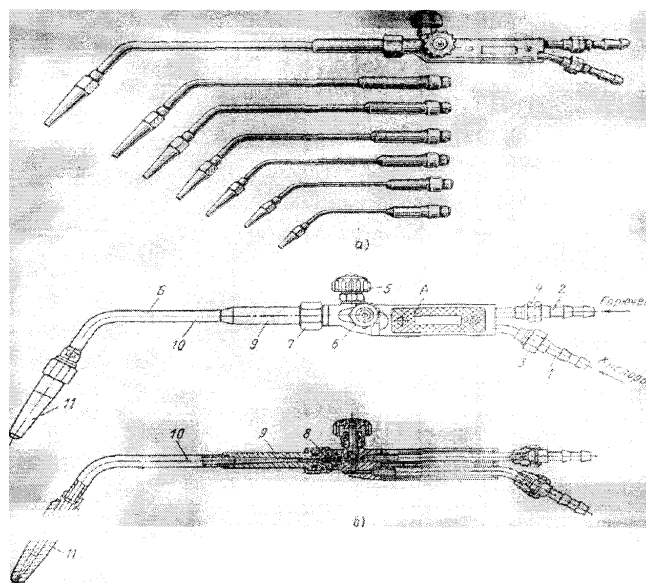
Универсальная ацетилено-кислородная сварочная горелка «Москва»: а — общий вид горелки с набором сменных наконечников; б— схема горелки
